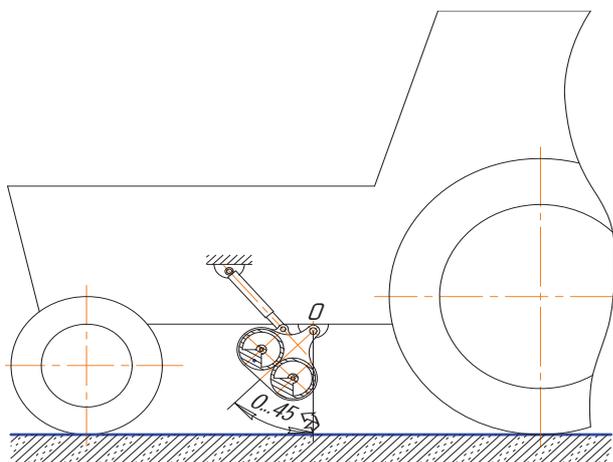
Расположение маятникового вибратора при движении трактора назад
